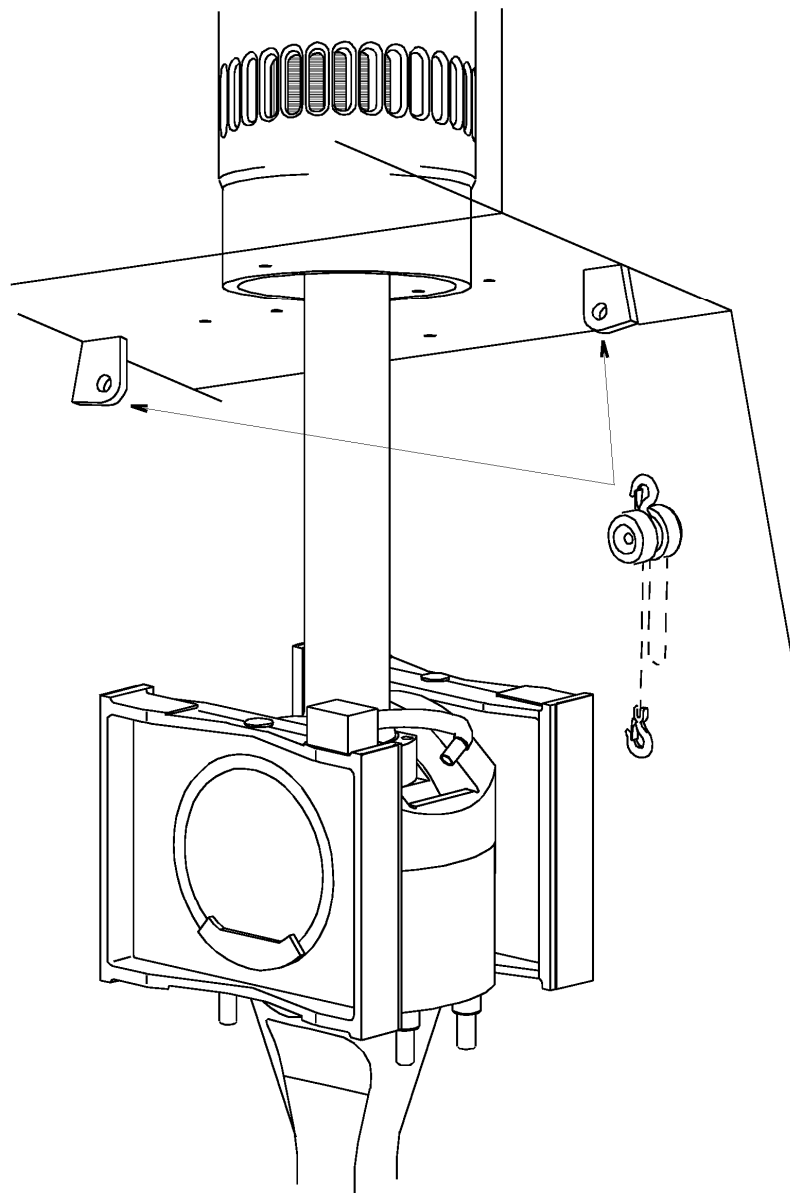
Розчалування штока поршня при розбиранні крейцкопфного вузла
